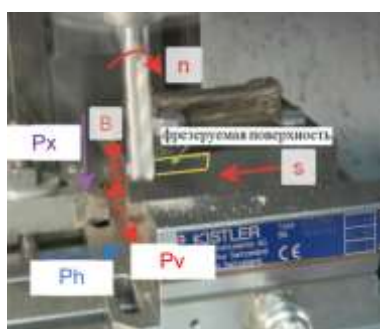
Установка заготовки на динамометре Kistler 9257B
